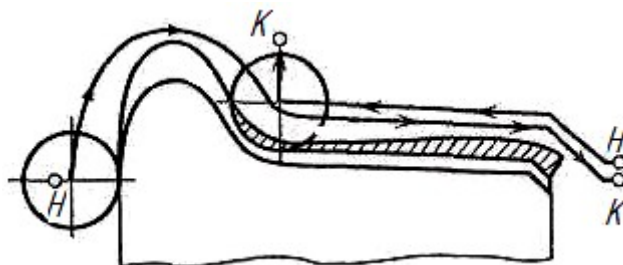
Схеми обробки профілю поверхні обода колеса чашковими різцями на колесотокарному верстаті моделі 1836А
